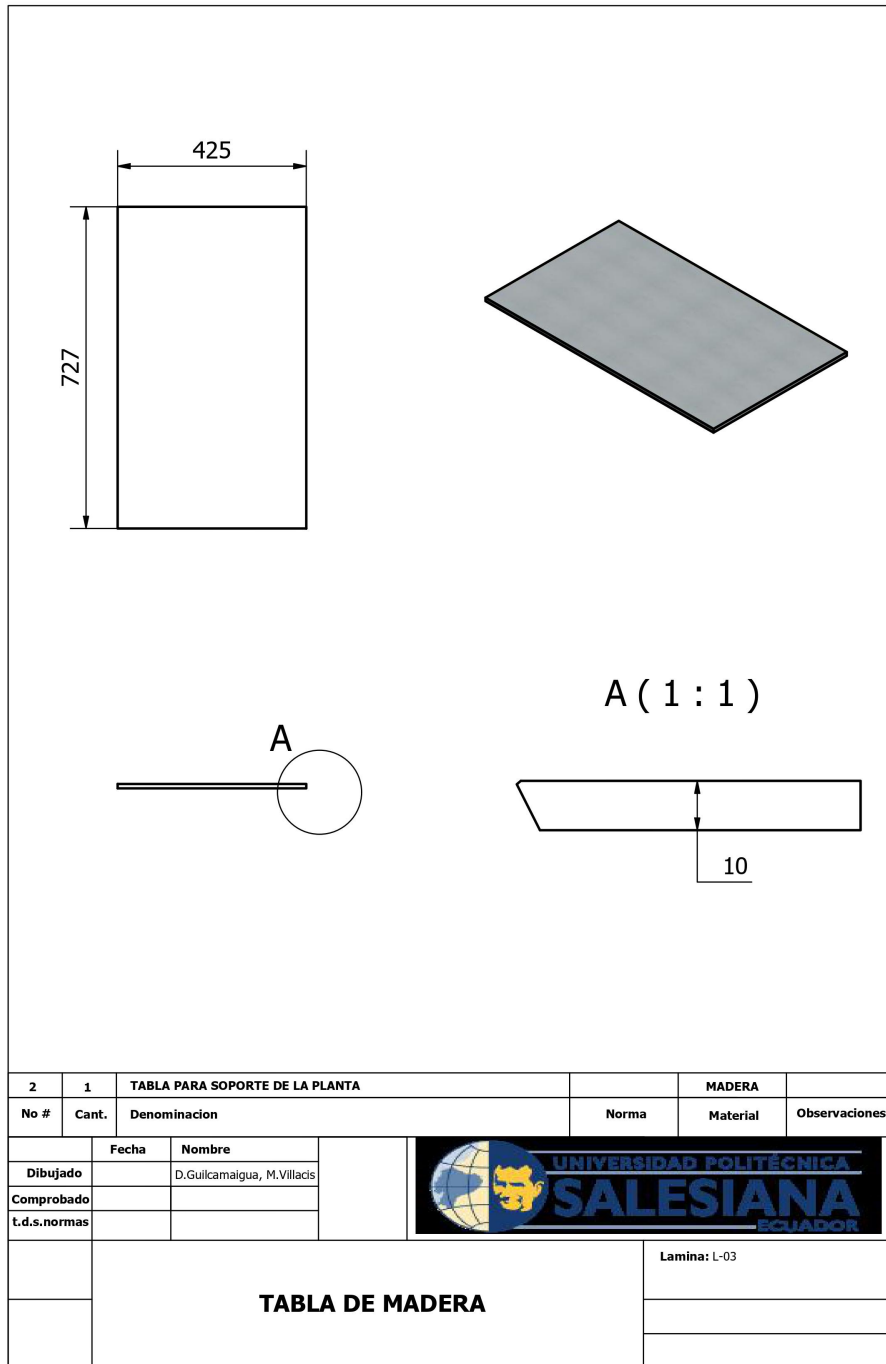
Plano de la tabla de soporte de la planta. Fuente: Los autores
